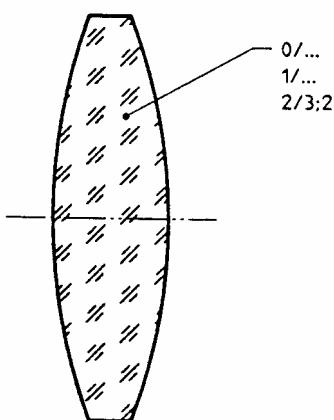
Пример обозначения допуска на неоднородность и свили
